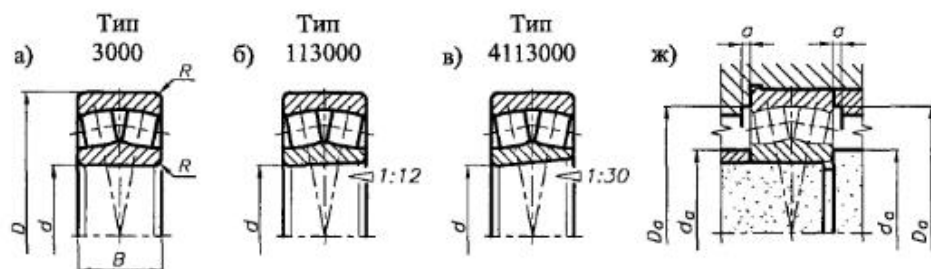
Габаритные и установочные размеры радиальных роликовых сферических двухрядных подшипников
